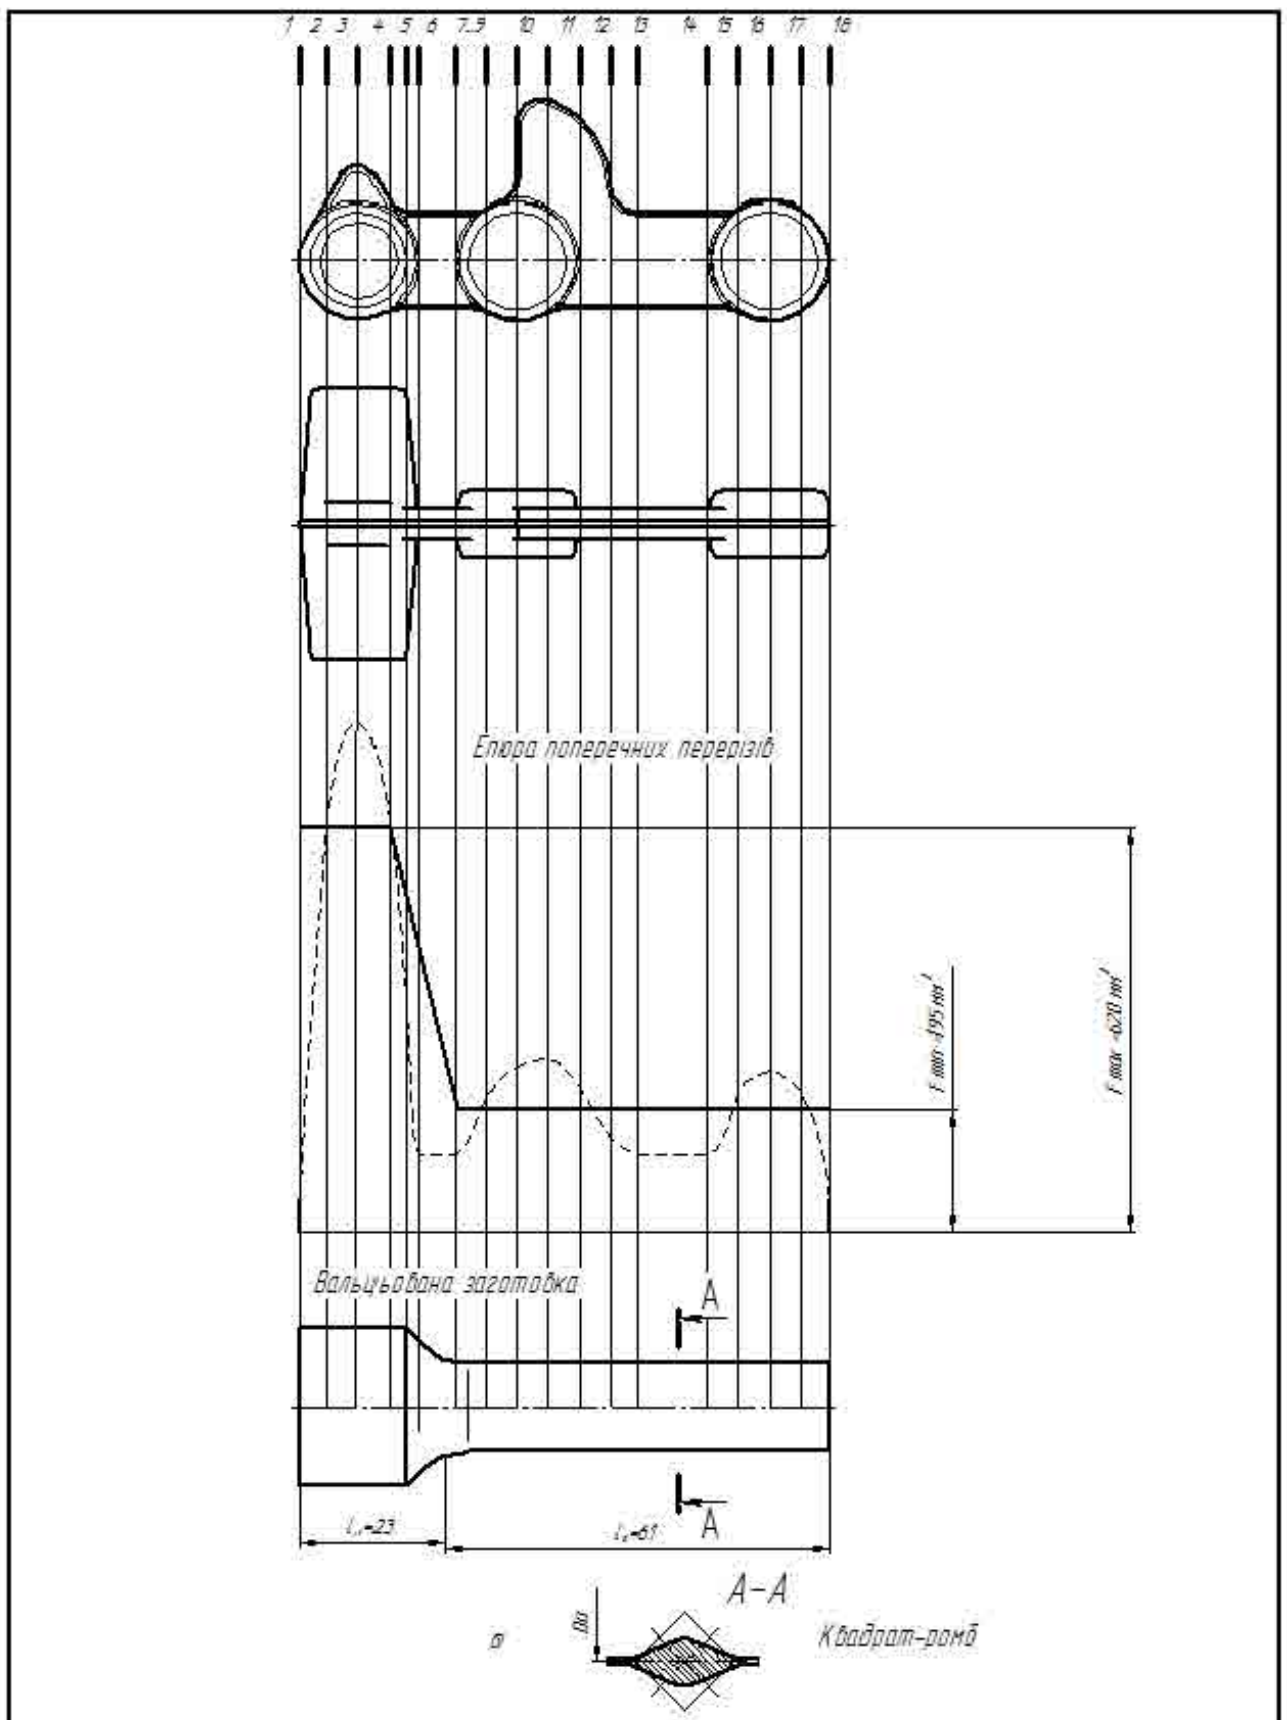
Еюра побудови вальцьованої заготовки
